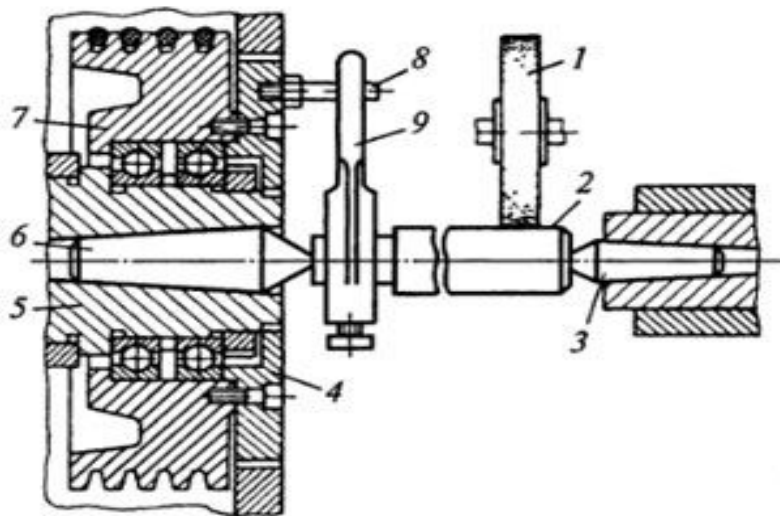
Установка заготовки в неподвижных центрах круглошлифовального станка
